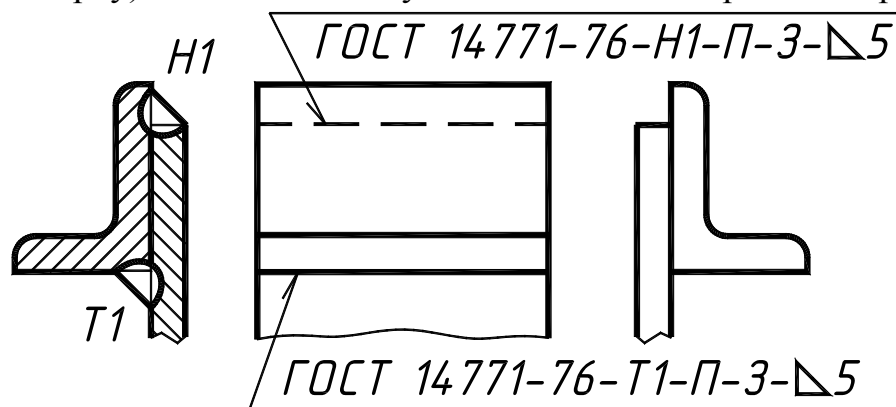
Нанесение условных обозначений сварных швов
